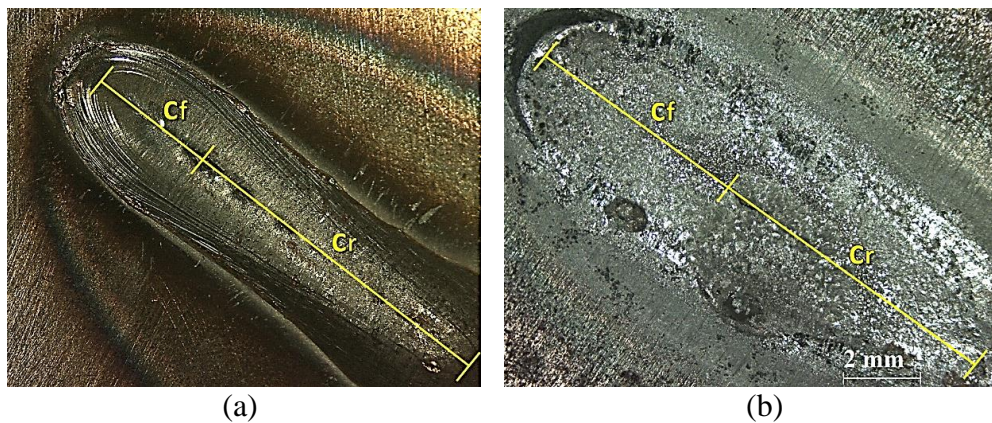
7 – Dimensões da poça de fusão. a) soldas MAG. b) soldas TIG.
